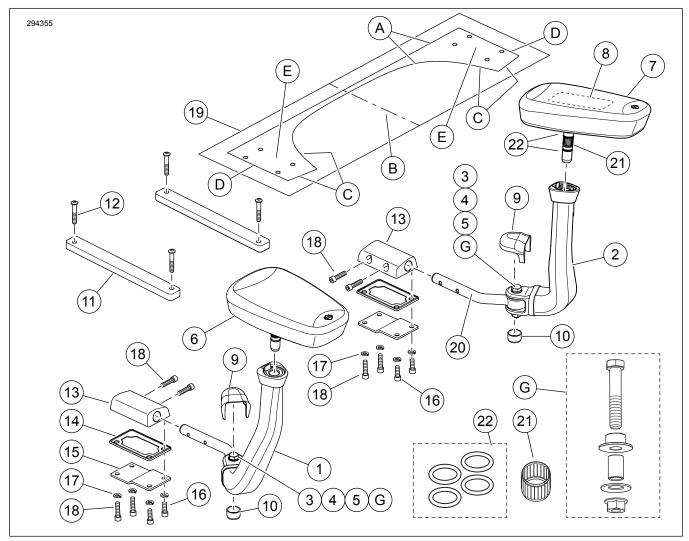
Pièces de rechange, kit d'accoudoir passager pour motocyclette à trois roues
